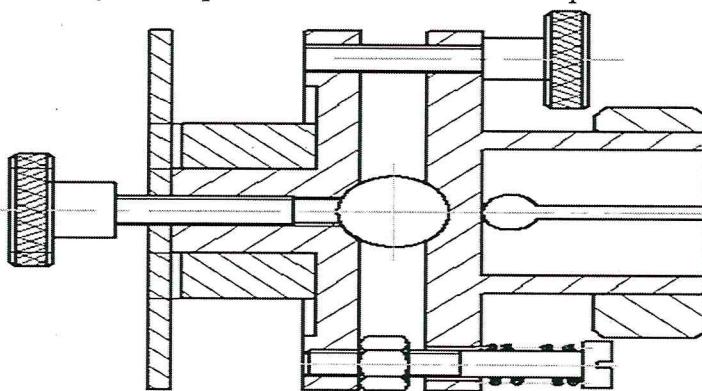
приспособление для установки многогранной призмы с присоединительным диаметром 12 или 20 мм.
